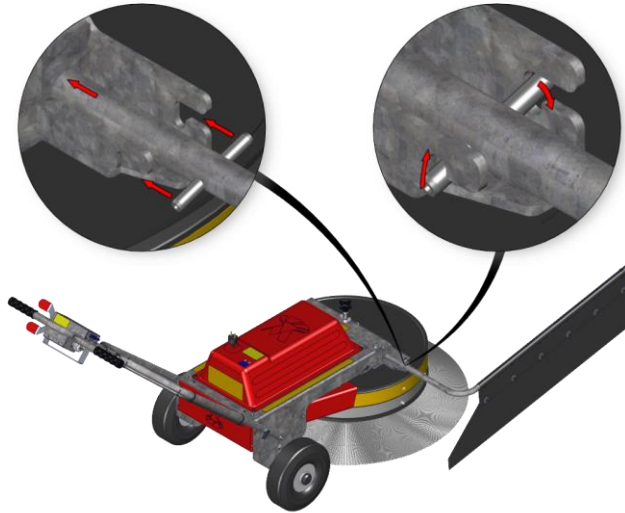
Anbau Schwadformer WR 870 Akku / Akku PRO
